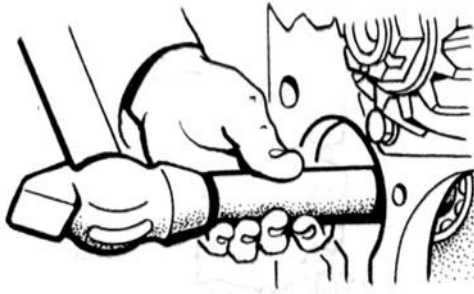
Випресування вала I передачі і заднього ходу
